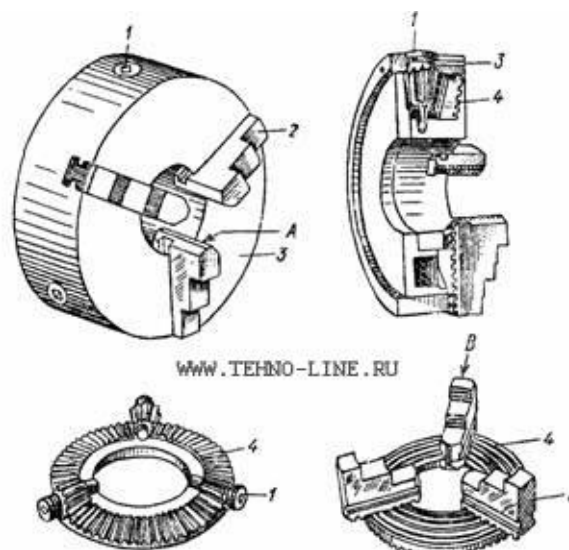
Самоцентрирующий трехкулачковый патрон и его детали
